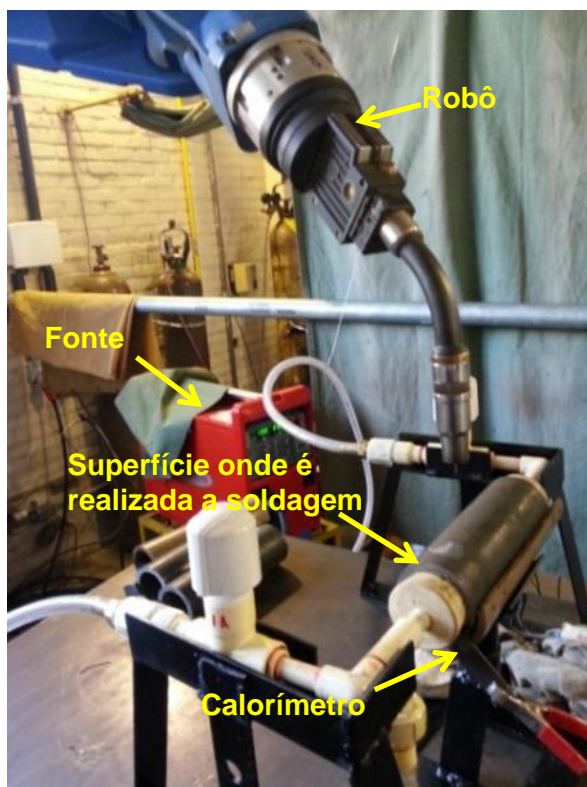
Equipamentos preparados para ser realizada a soldagem.
